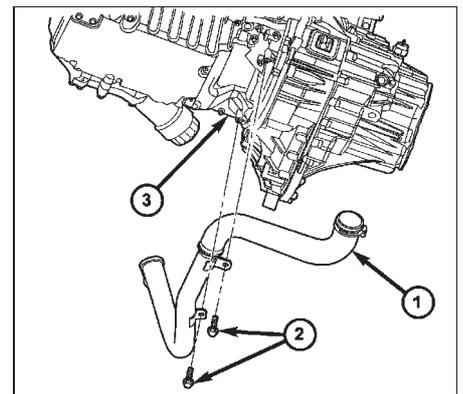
Крепление трубы охладителя наддувочного воздуха. 1 - труба охладителя, 2 - болт (2), 3 - проставка опоры силового агрегата.
